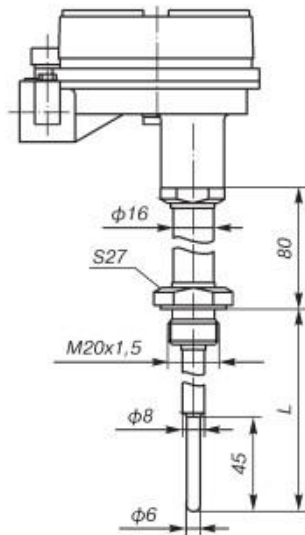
Габаритные и присоединительные размеры Метран-286
